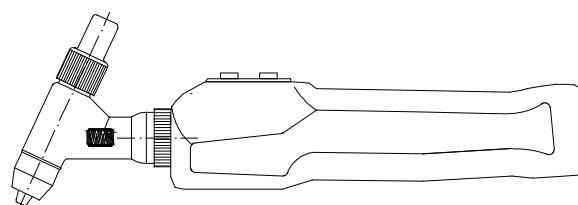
PWH 150 горелка для ручной сварки с кнопкой
